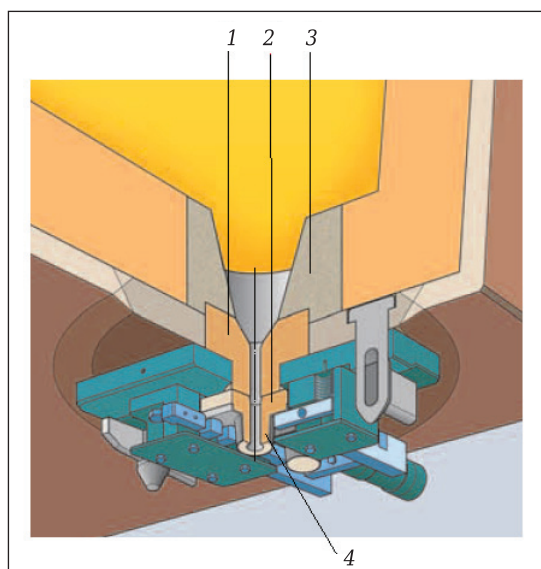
Комплект огнеупорного оборудования разливочного отверстия: 1 — гнездовой блок; 2 — стакан-дозатор; 3 — набивная смесь; 4 — втулка стакан-дозатора
